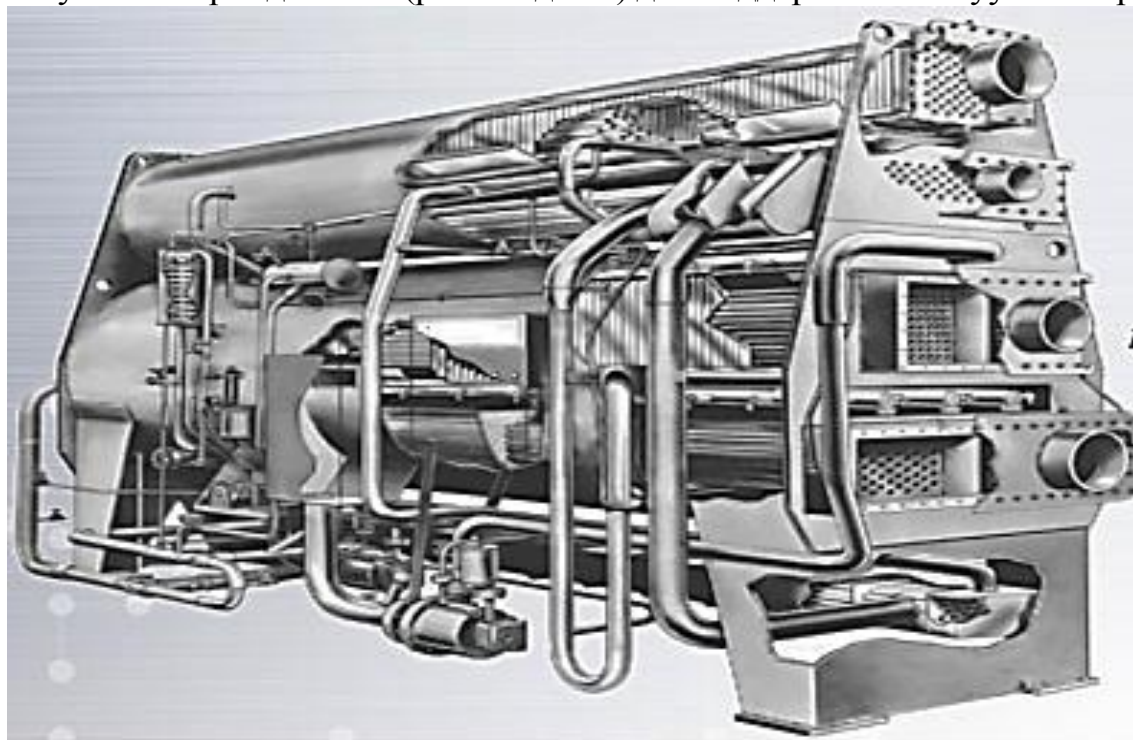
Общий вид АБТН с разрезами по корпусу
